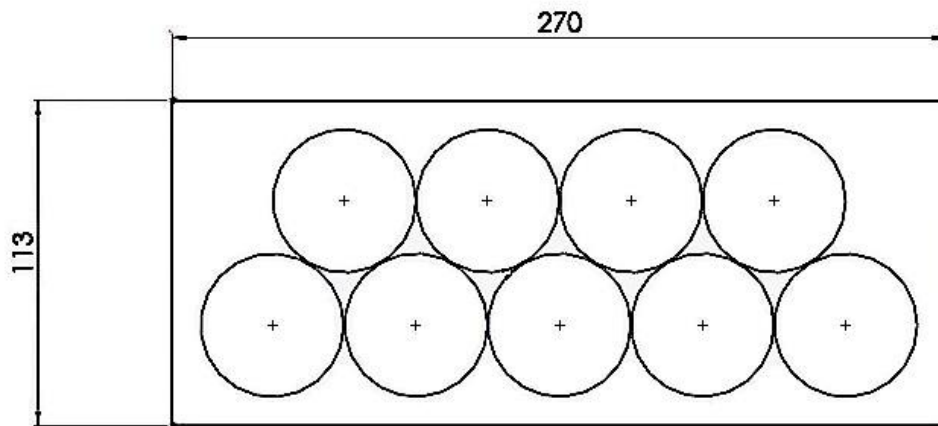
Vista en planta de la caja de cementación. Cotas en mm
